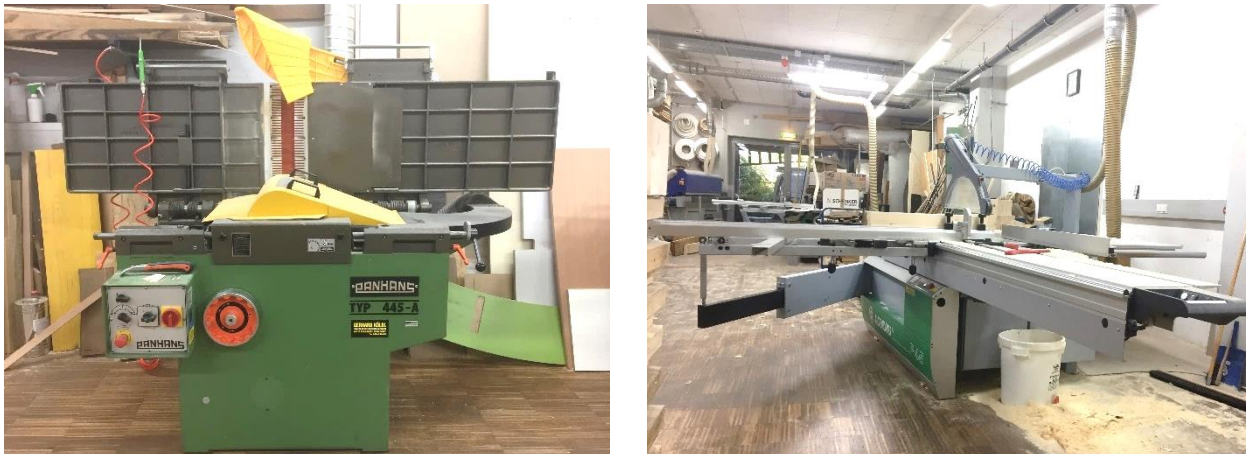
Holzbearbeitungsmaschinen
